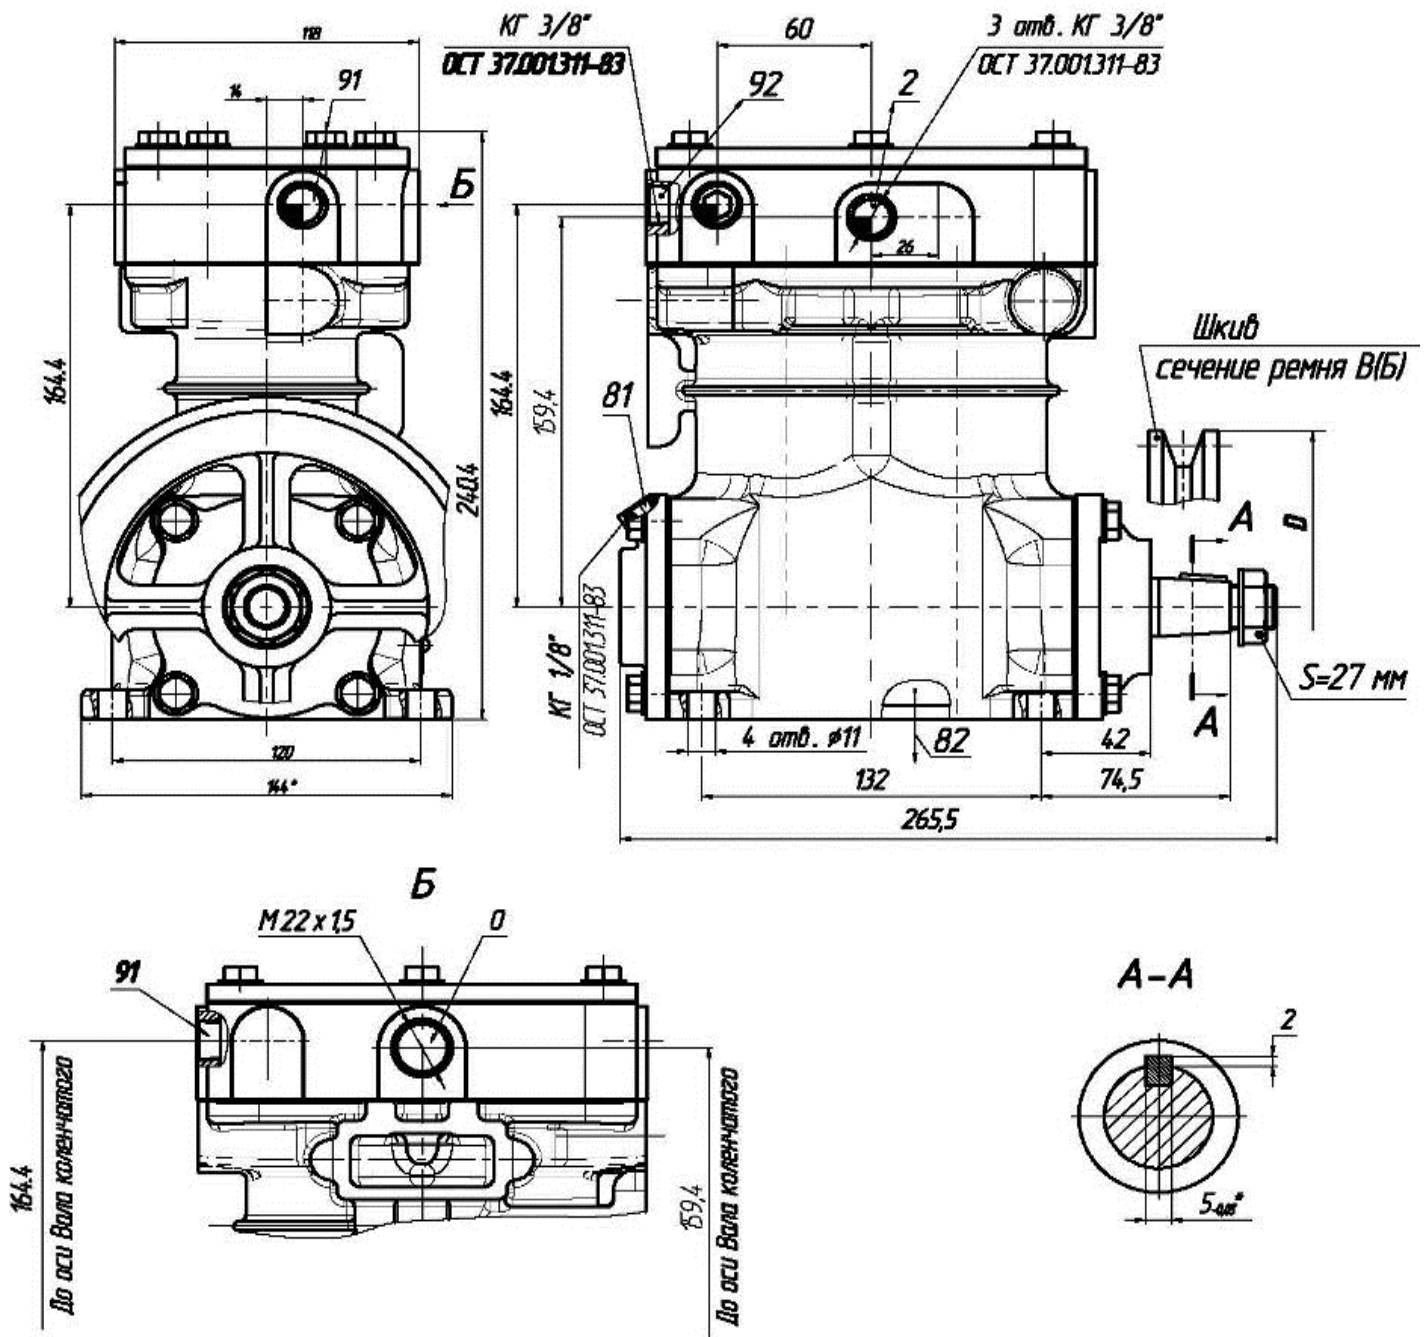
Присоединительные и установочные размеры компрессоров АМ.3509012-16-20 (диаметр Шкива $D=144$ мм) и АМ.3509012-161-20 (диаметр Шкива $D=172$ мм).
